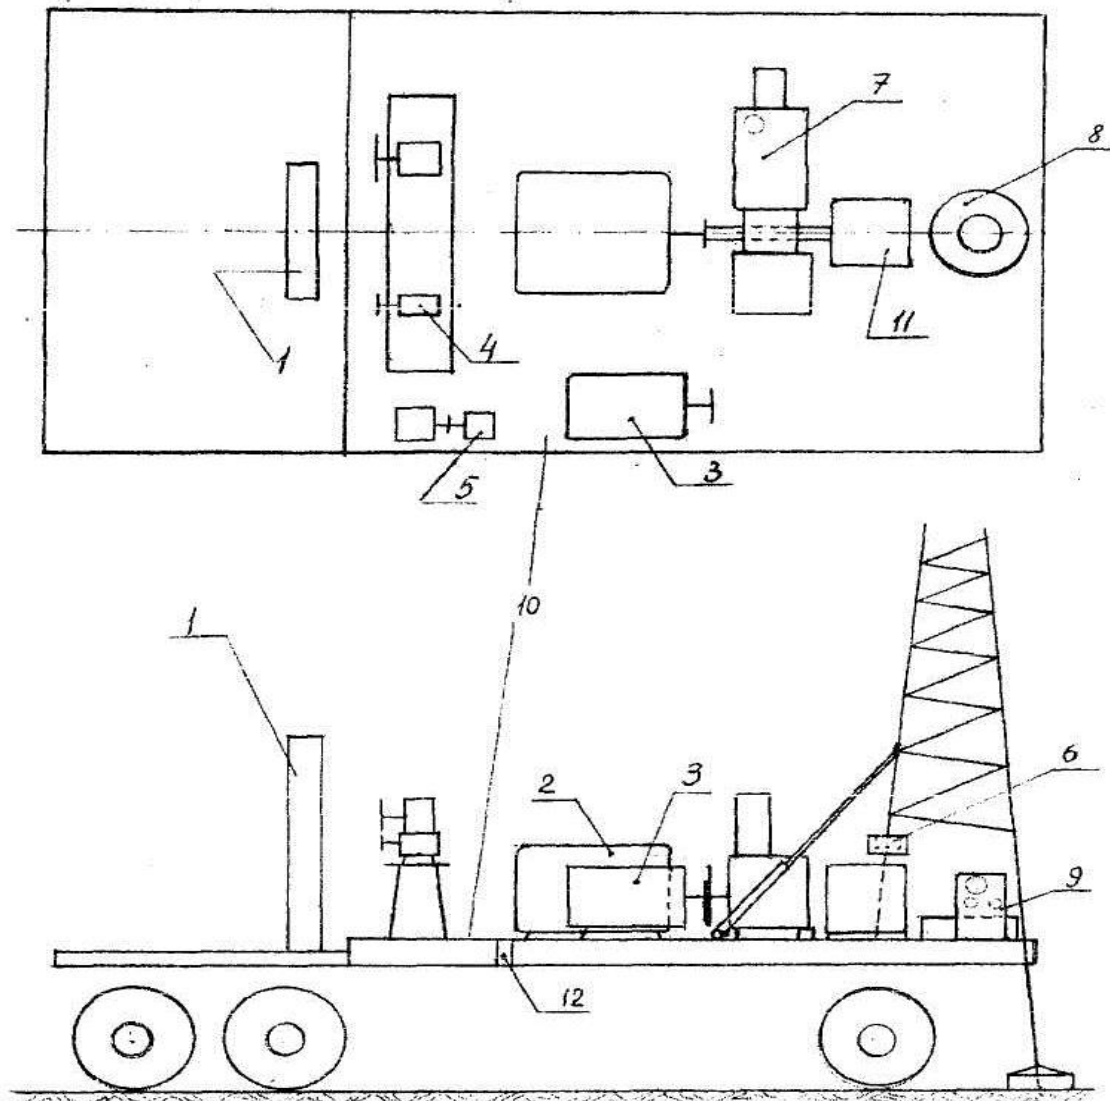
Схема расположения оборудования на платформе буровой установки УРБ-3А3-Э
